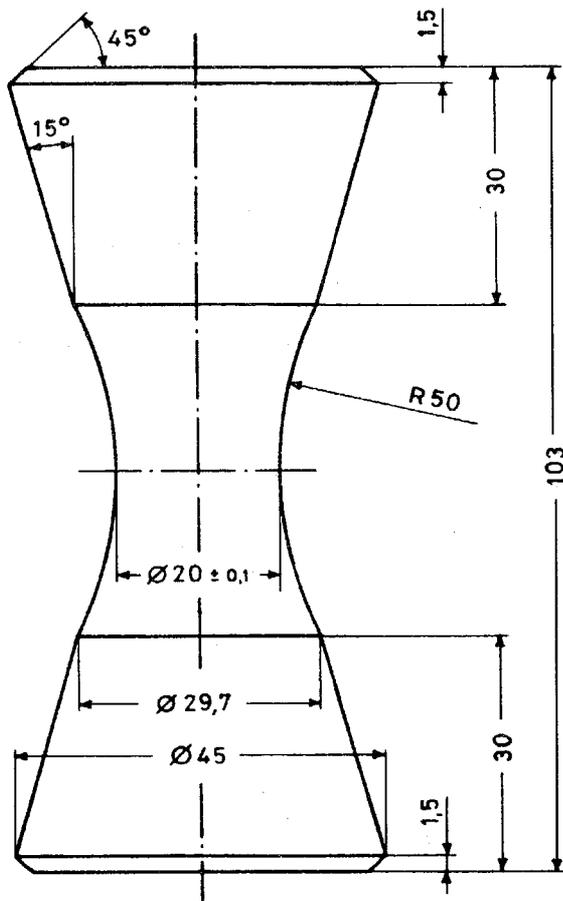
Dimensioni in mm della provetta di trazione per blocchi e barre.
